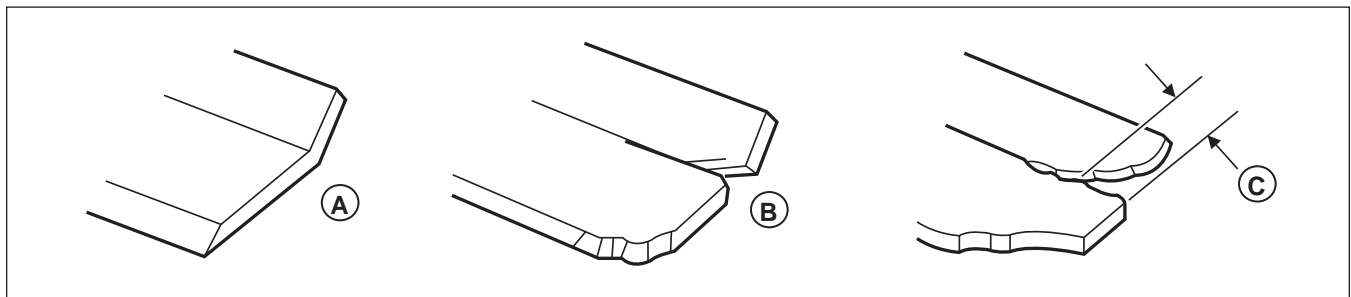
Inspección de los elevadores por aire de las cuchillas del cortacésped
